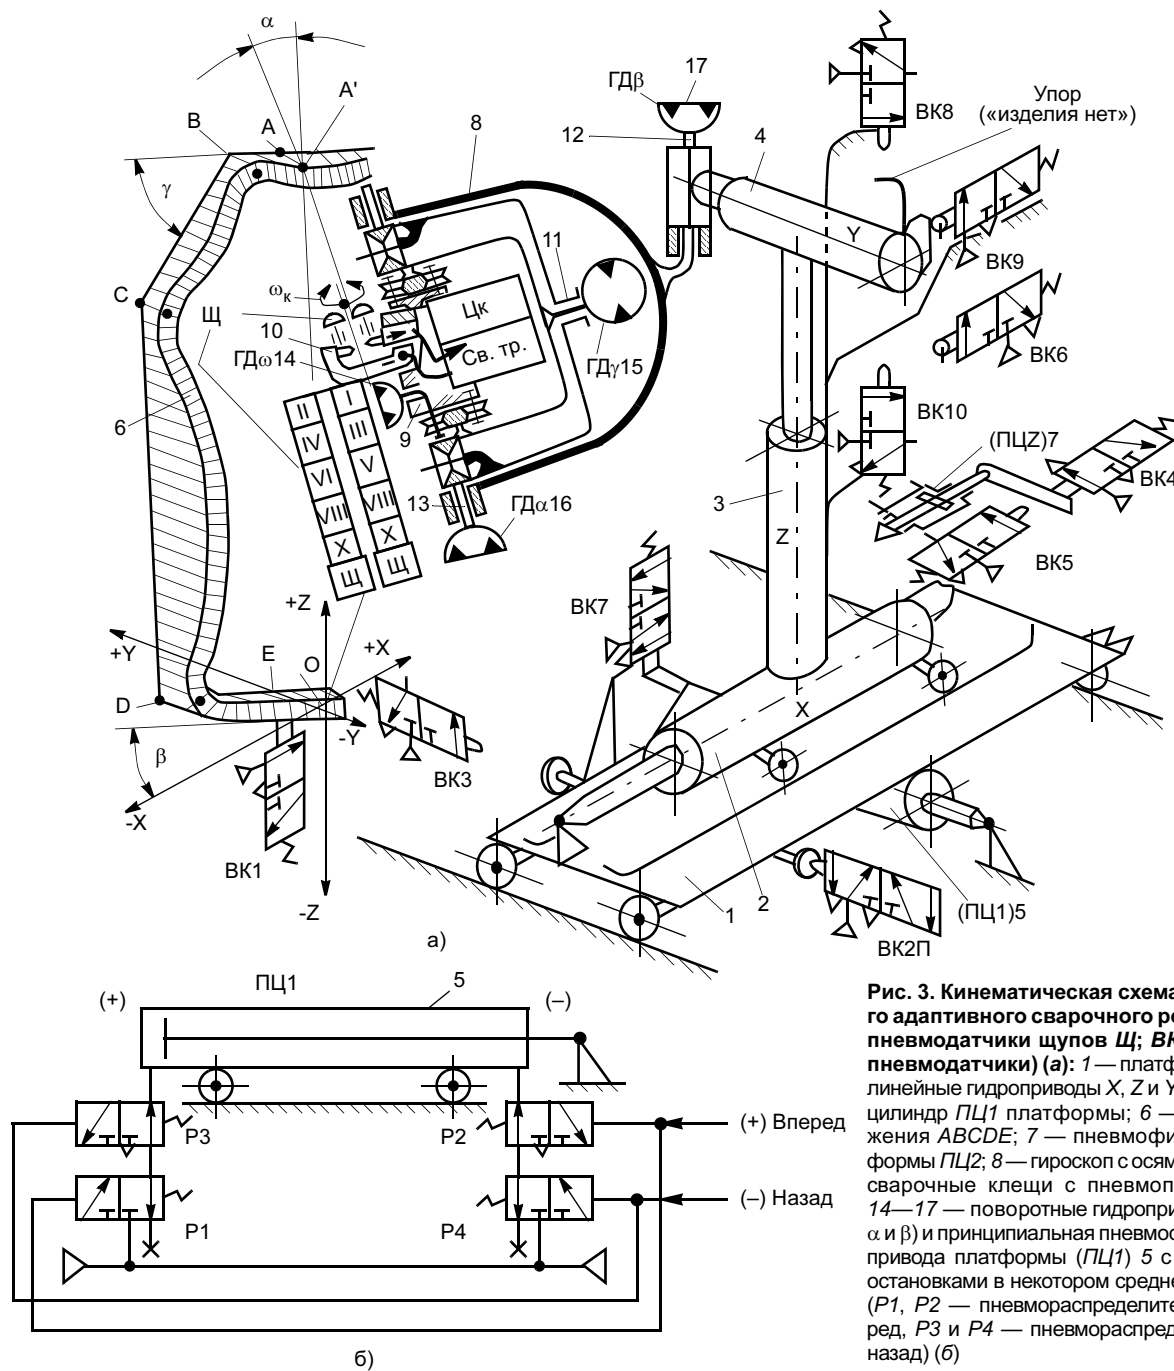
Кинематическая схема консольного адаптивного сварочного робота (1...X — пневмодатчики щупов Щ; ВК — путевые пневмодатчики) (а): 1 — платформа; 2—4 — линейные гидроприводы X, Z и Y; 5 — пневмоцилиндр ПЦ1 платформы; 6 — контур слежения ABCDE; 7 — пневмофиксатор платформы ПЦ2; 8 — гироскоп с осями 9—13; 10 — сварочные клещи с пневмоприводом Цк; 14—17 — поворотные гидроприводы ГД (ω , γ , α и β) и принципиальная пневмосхема пневмопривода платформы (ПЦ1) 5 с управлением остановками в некотором среднем положении (P1, P2 — пневмораспределители хода вперед, P3 и P4 — пневмораспределители хода назад) (б)
